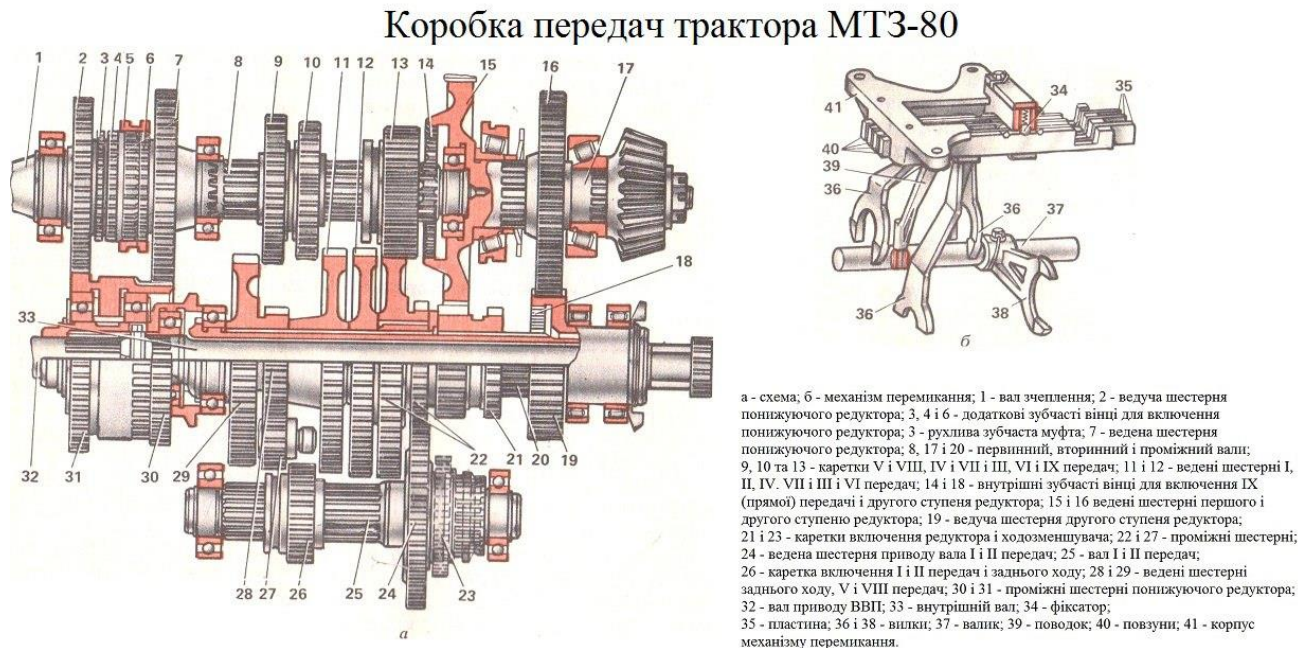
Схема коробки передач трактора МТЗ -80[2]
